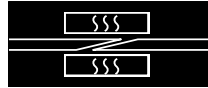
Vue d'ensemble de la presse modèle PM-09/160W
